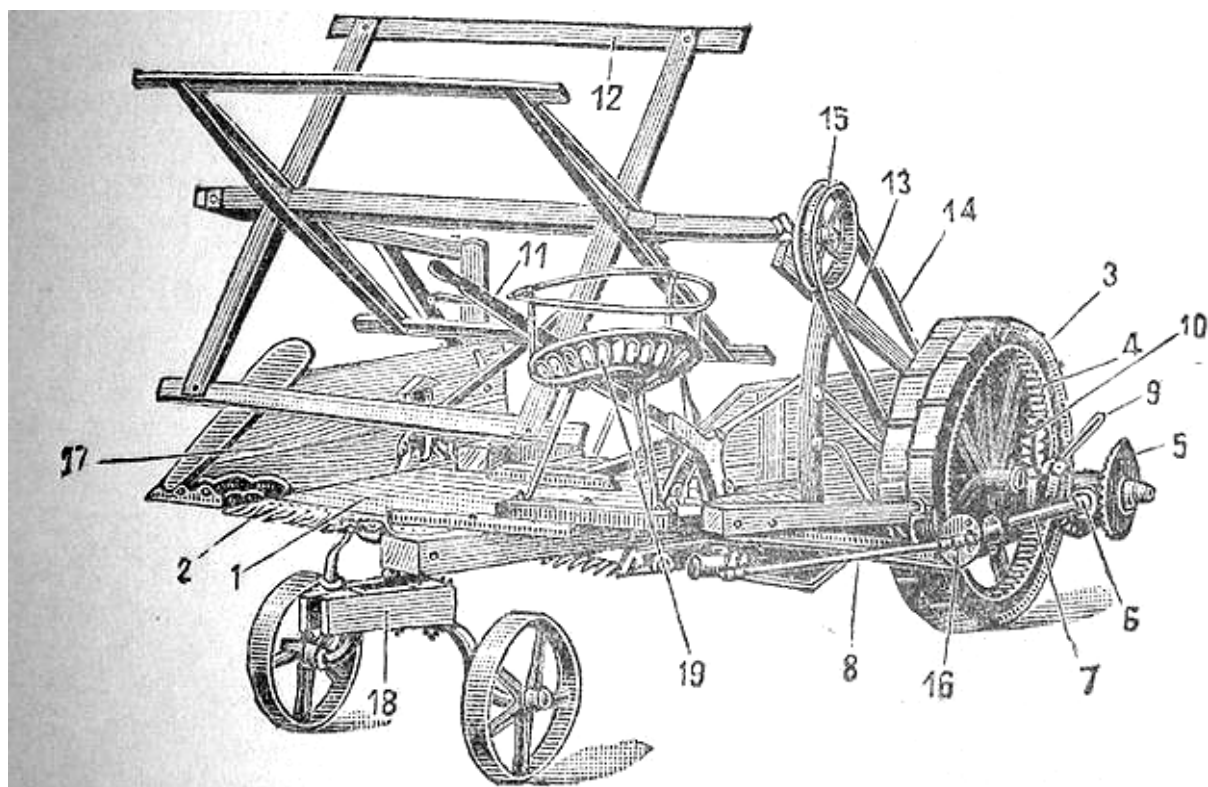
Лобогрейка завода «Красный Аксай»: 1 — платформа; 2 — пальцевый брус; 3 — ходовое колесо; 4 — большая цилиндрическая шестерня; 5 — большая коническая шестерня; 6 — малая коническая шестерня; 7 — косогонный вал; 8 — шатун; 9 — подъемный рычаг ходового колеса; 10 — левая стойка с кулисой; 11 — рычаг наклона платформы; 12 — мотовило; 13 — наклонные бруски мотовила; 14 — ремень передачи к мотовилу; 15 — шкив ременной передачи к мотовилу; 16 — диск кривошипа; 17 — полевой делитель; 18 — передок; 19 — переднее сиденье.
